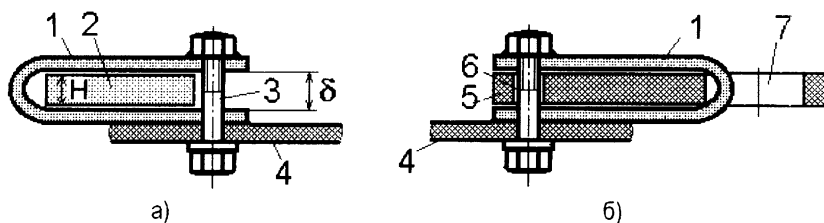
Конструкция U-образной монтажной планки и схемы ее крепления на силовой балке (а) и на пластине со сквозными отверстиями (б):
